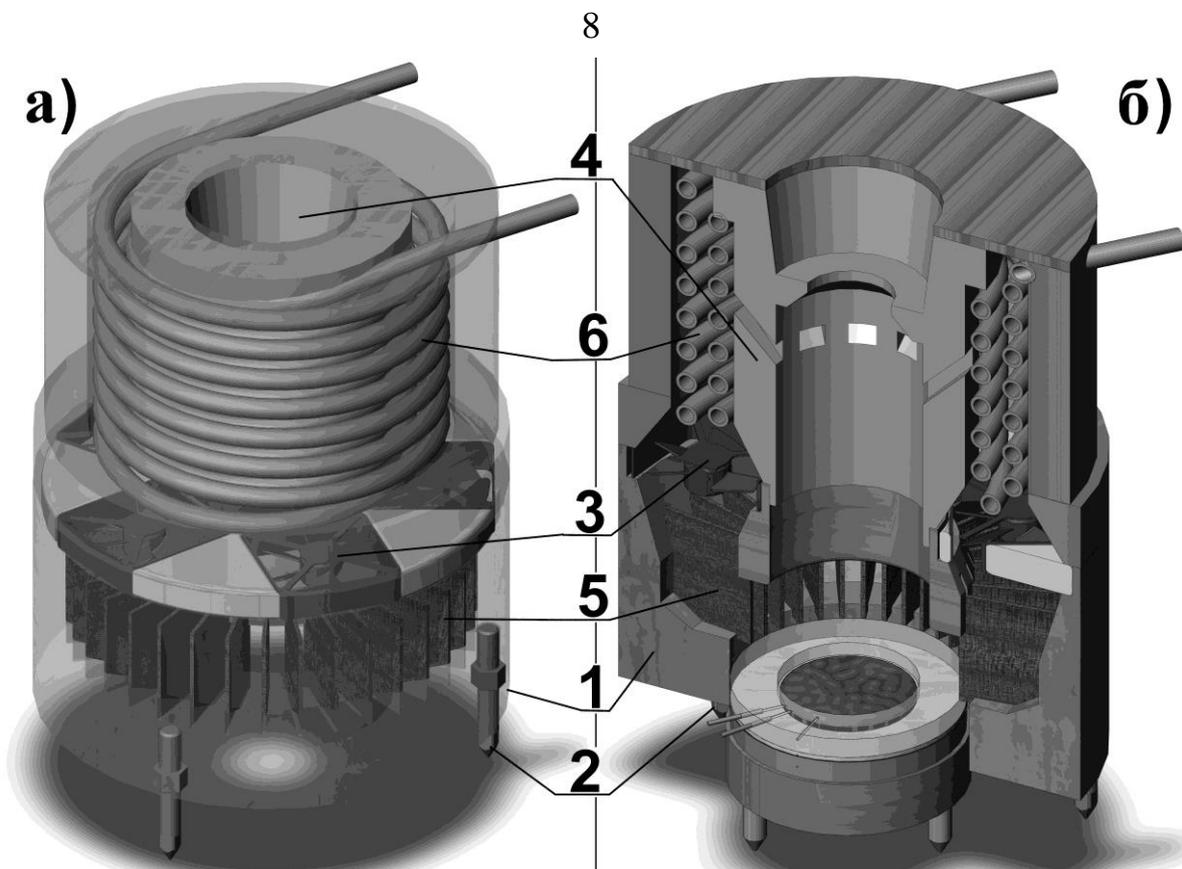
Система термостатирования: а) внешний вид с прозрачным корпусом; б) вид диаметрального сечения.
